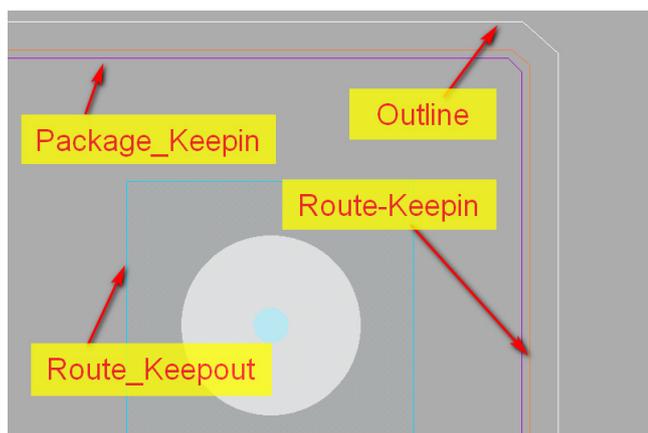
Контрольные зоны для размещения и трассировки в OrCAD PCB Editor
